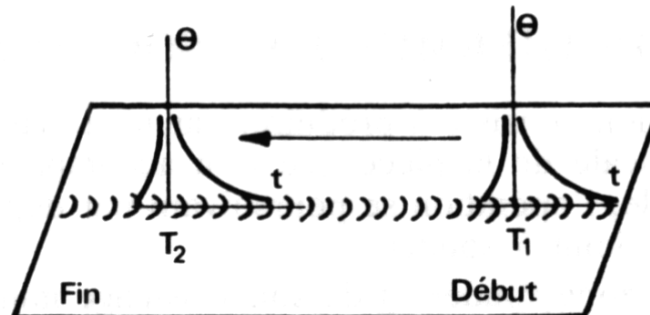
Identité de répartition thermique en cours de soudage. [BERT 88]
